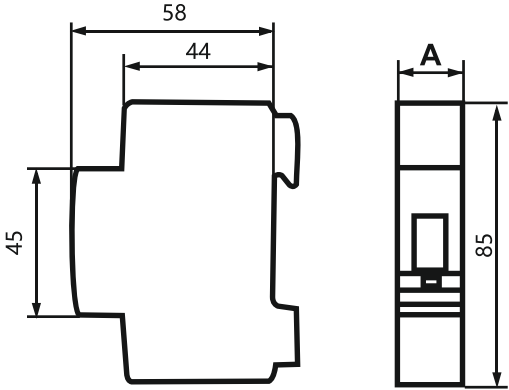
Габаритные размеры контакторов AF8M-16
